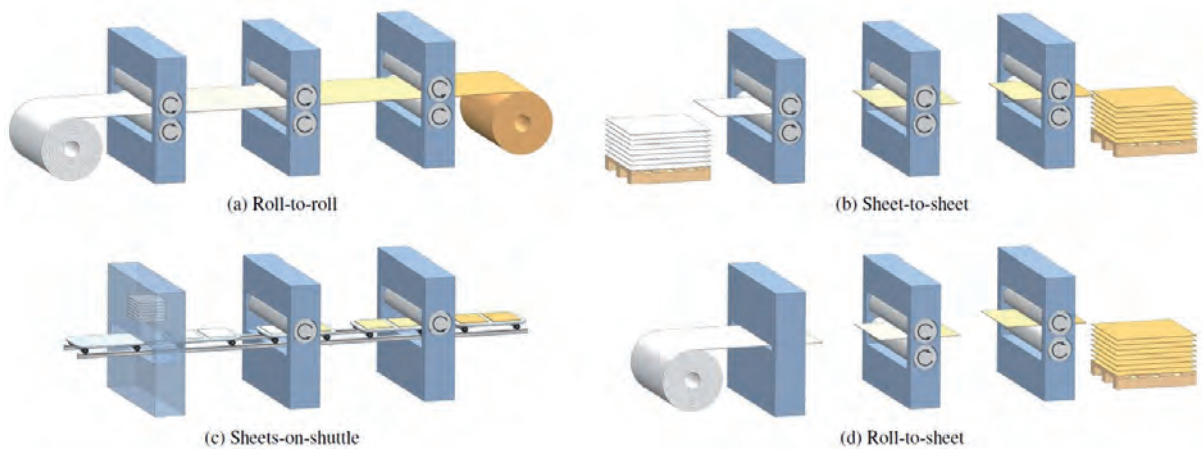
Die vier Methoden des Substrattransports: Roll to Roll, Sheet to Sheet, Roll to Sheet und Sheets on Shuttle
